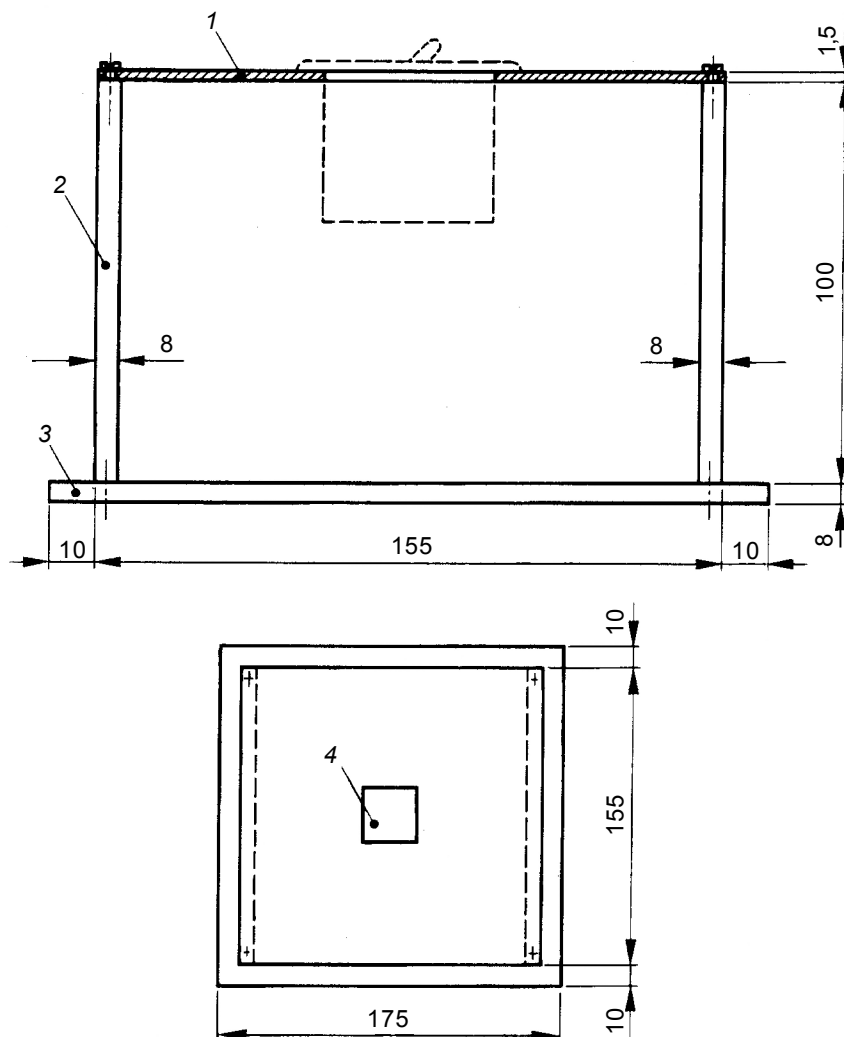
Монтажна опорна рама для випробовування на механічний удар (9.13.2)
